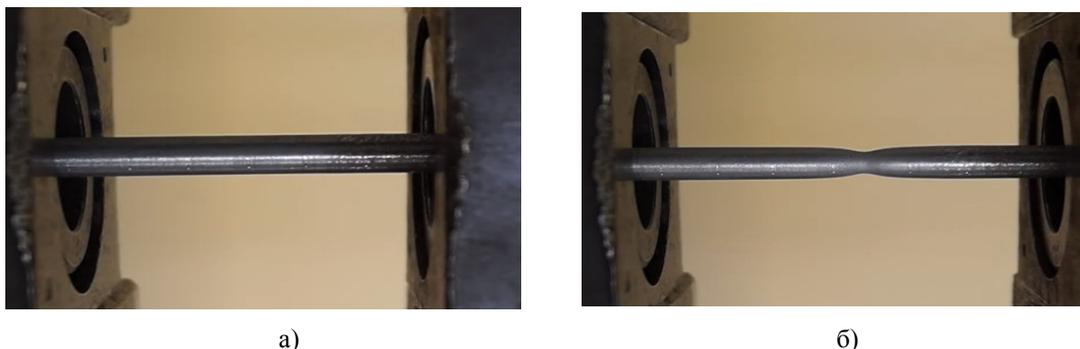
Испытание образца на статическое растяжение: а) образец до испытания; б) образец перед разрушением [2]
